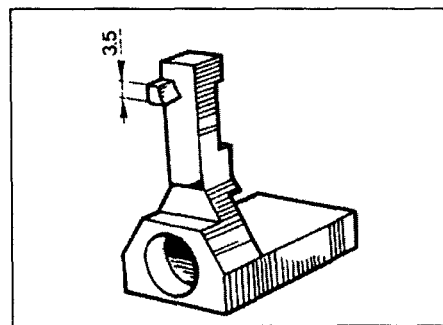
Приспособление Citroën/Peugeot для регулировки пускового устройства
